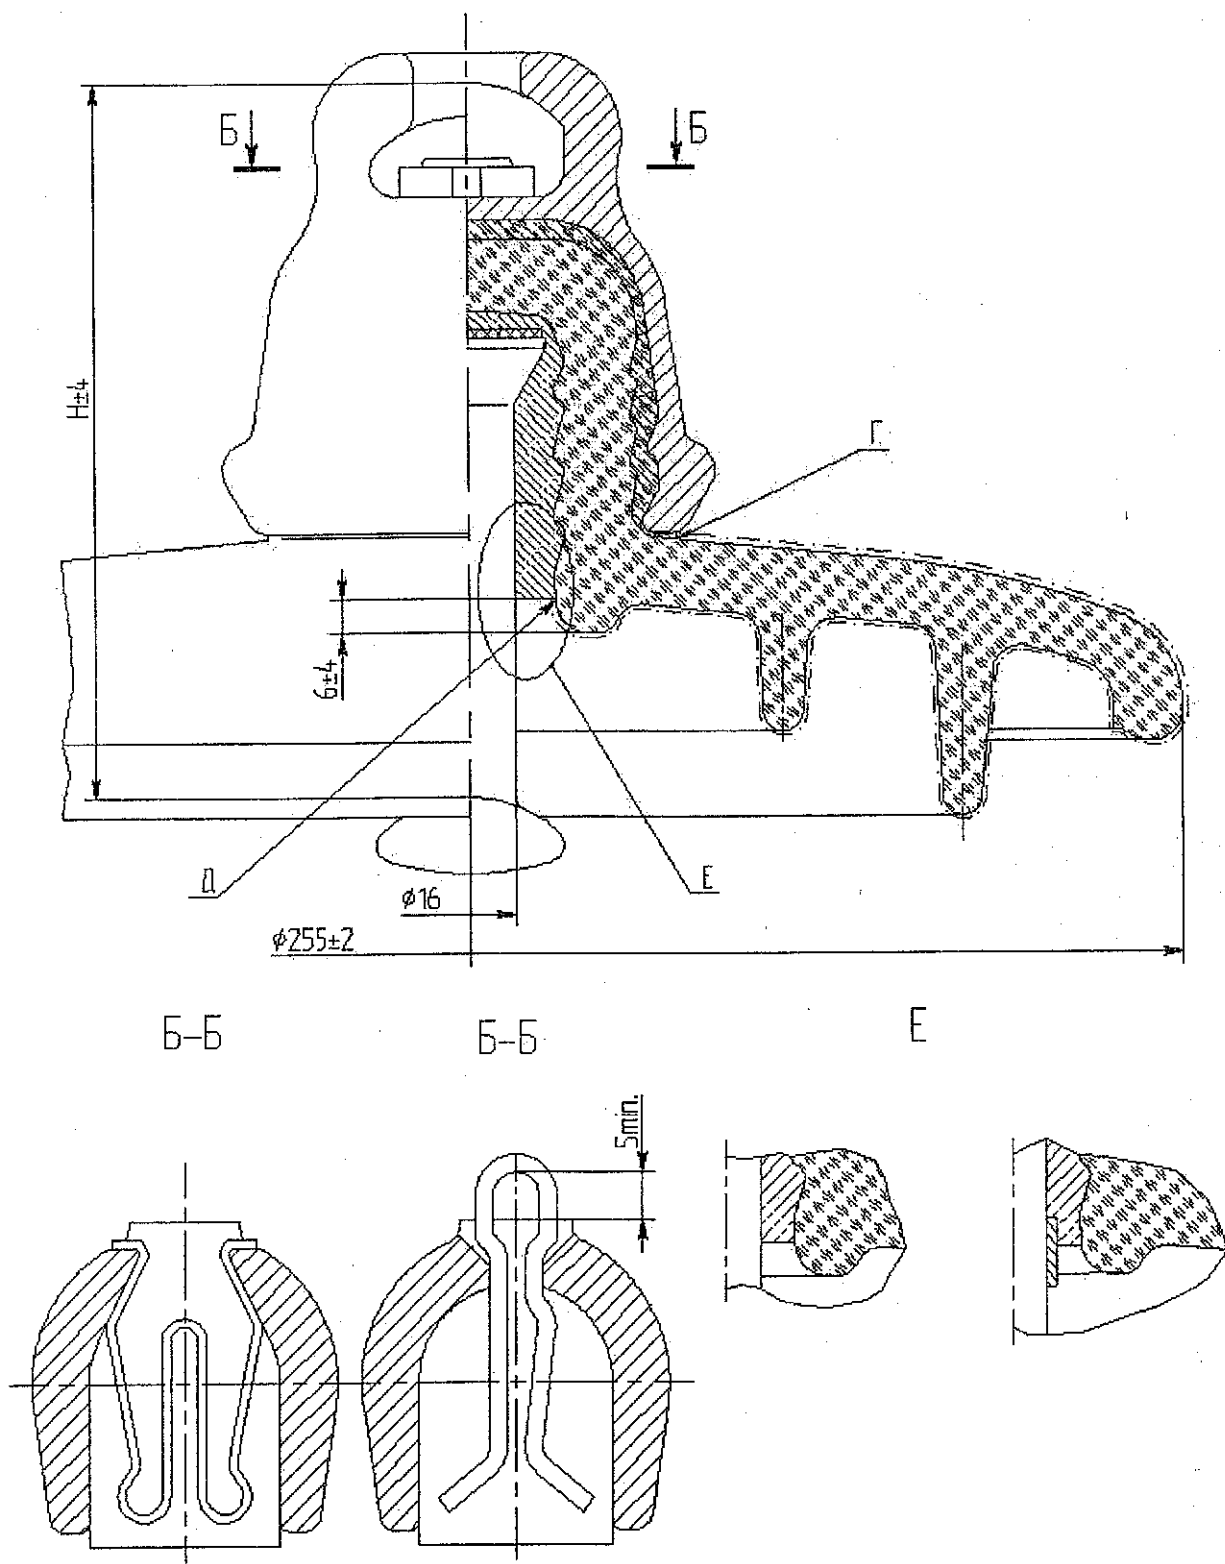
Габаритные, присоединительные и установочные размеры изолятора ПС70Е
